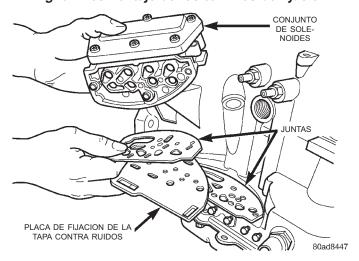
Desmontaje del conjunto de solenoides SENSOR DE POSICION DE LA TRANSMISION
